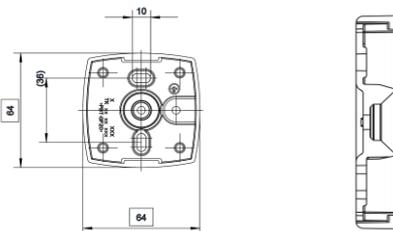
Vue en plan et en coupe de la plaque d'adaptation
